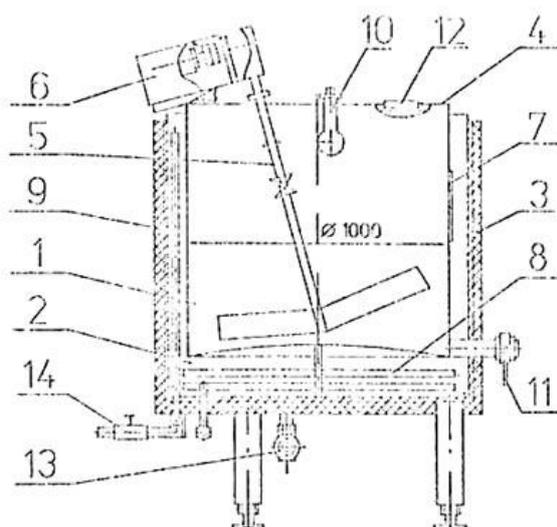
Устройство заквасочной установки ОЗУ-0,35
